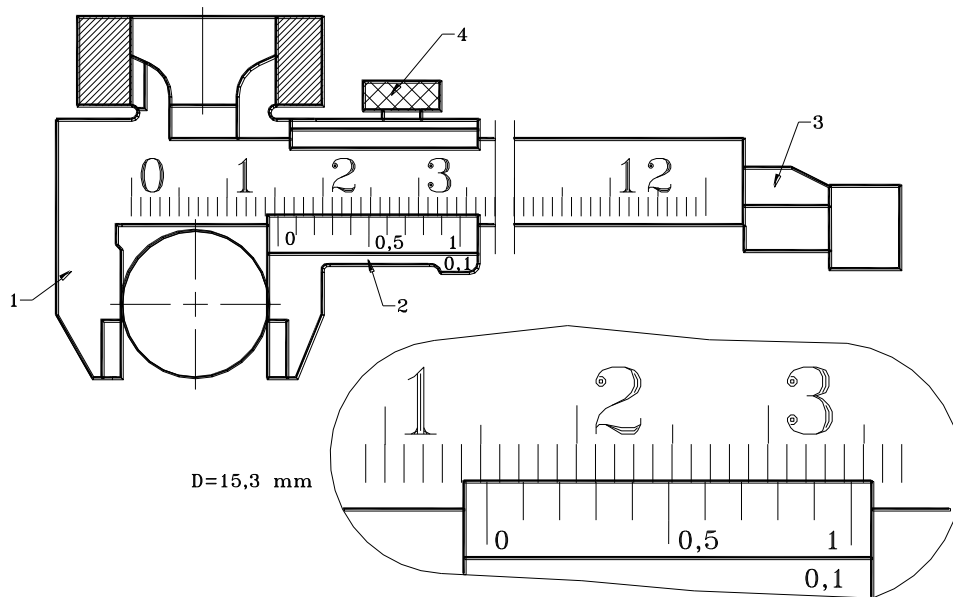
Construção do paquímetro e exemplos da sua utilização.
